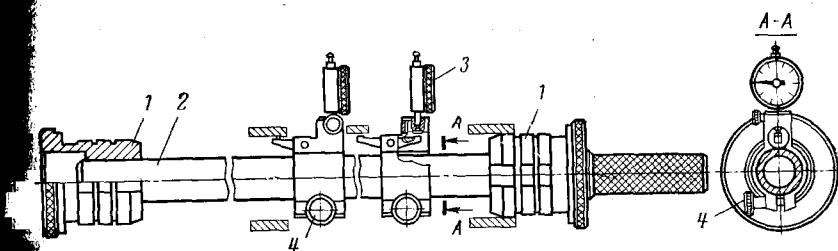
Приспособление для контроля соосности гнезд вкладышей коренных подшипников
